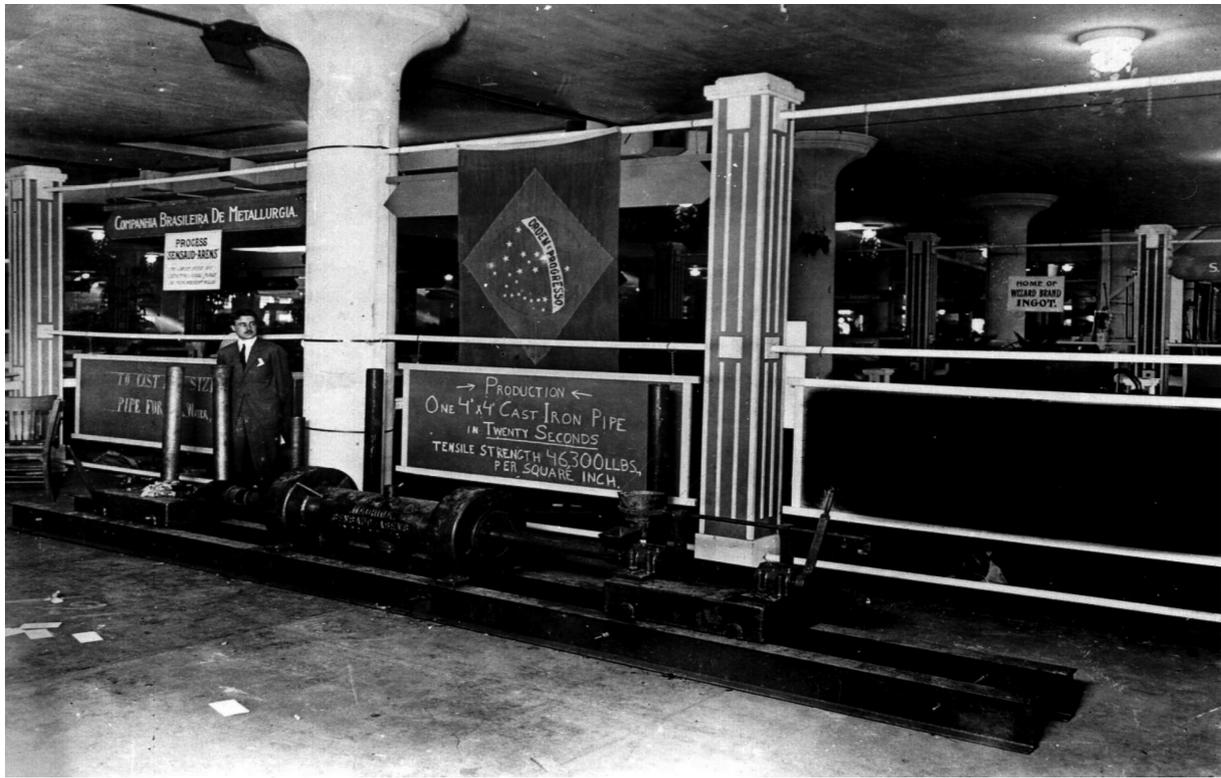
1 – Vista do estande montado por De Lavaud, por ocasião da American Foundrymen's convention, em Cleveland, EUA, em 1916.
